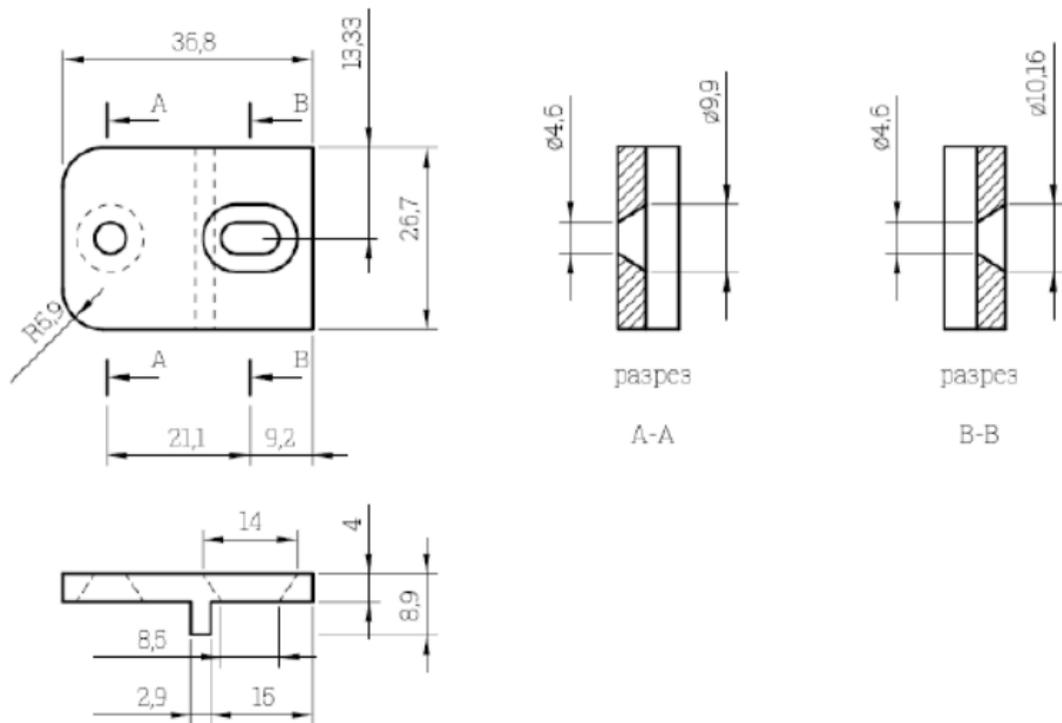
Габаритные размеры пластиковых кронштейнов для крепления корпуса типа К1
